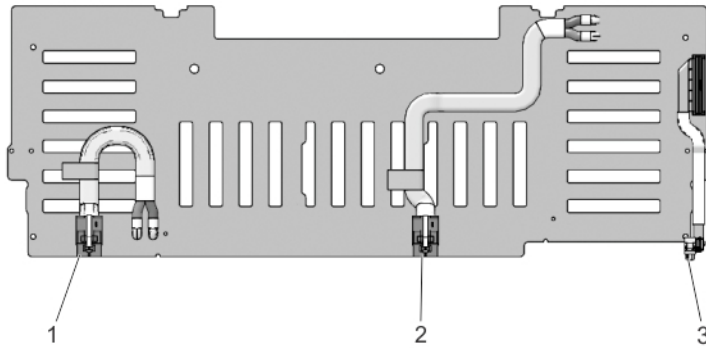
Fond de panier SAS/SATA (x24) de 2,5 pouces : vue arrière
